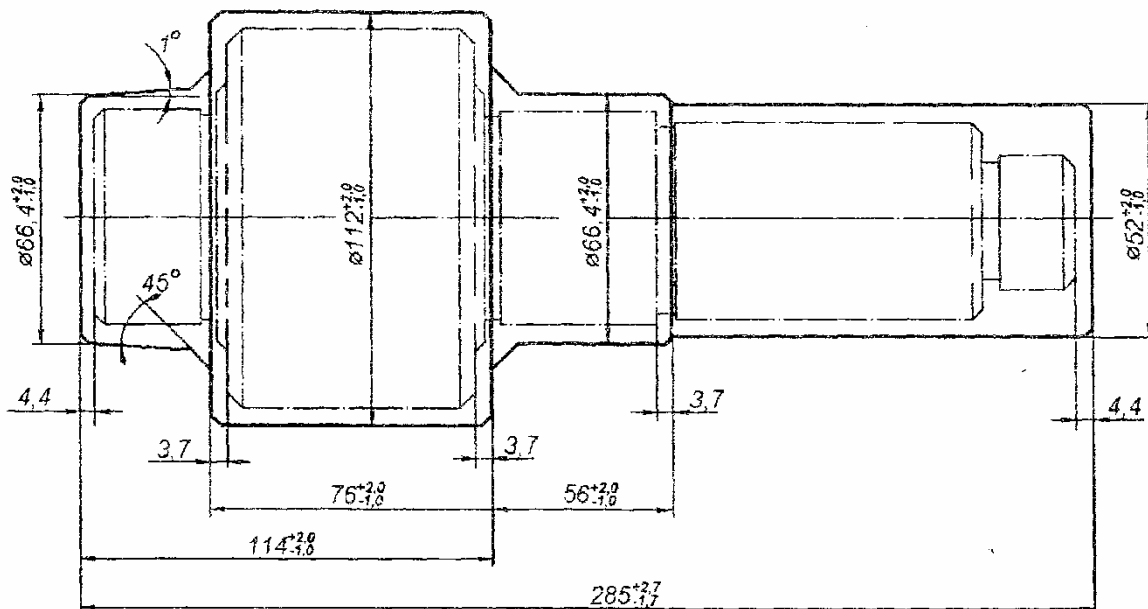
Заготовка шестерни ведущей (Рисунок 3) с начисленными припусками
